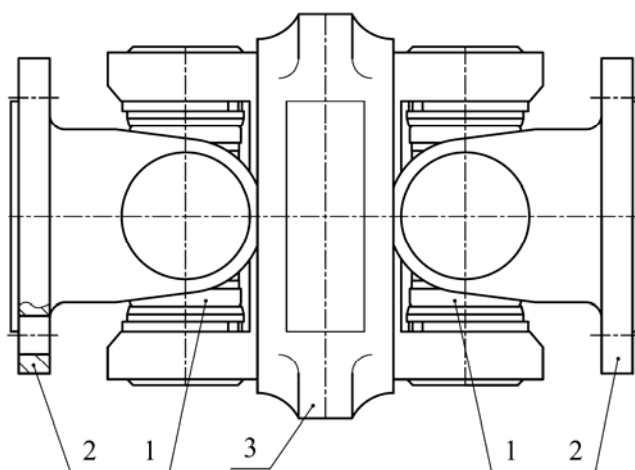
Сдвоенный шарнир двигателя DETROIT DIESEL.
